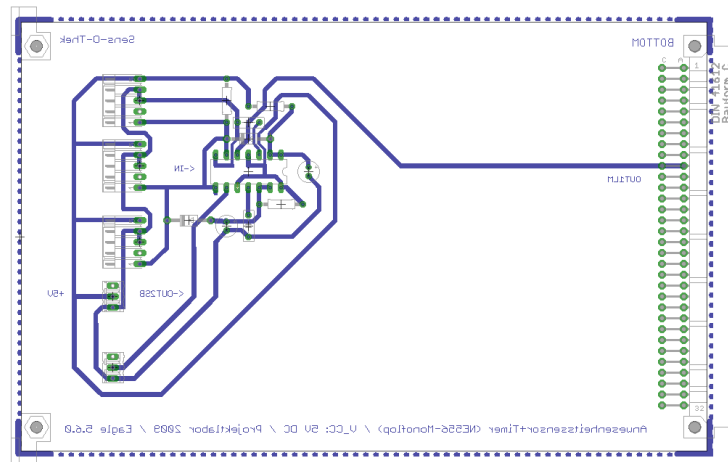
Platinen-Layout (ohne Massefläche), Eagle 5.6.0 Board
